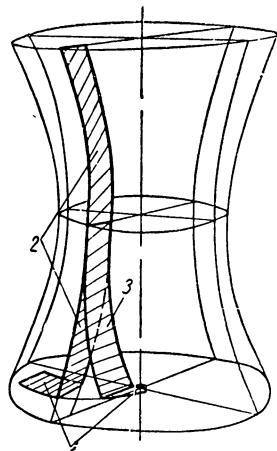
Процесс зацепления червяка с зубом колеса.
